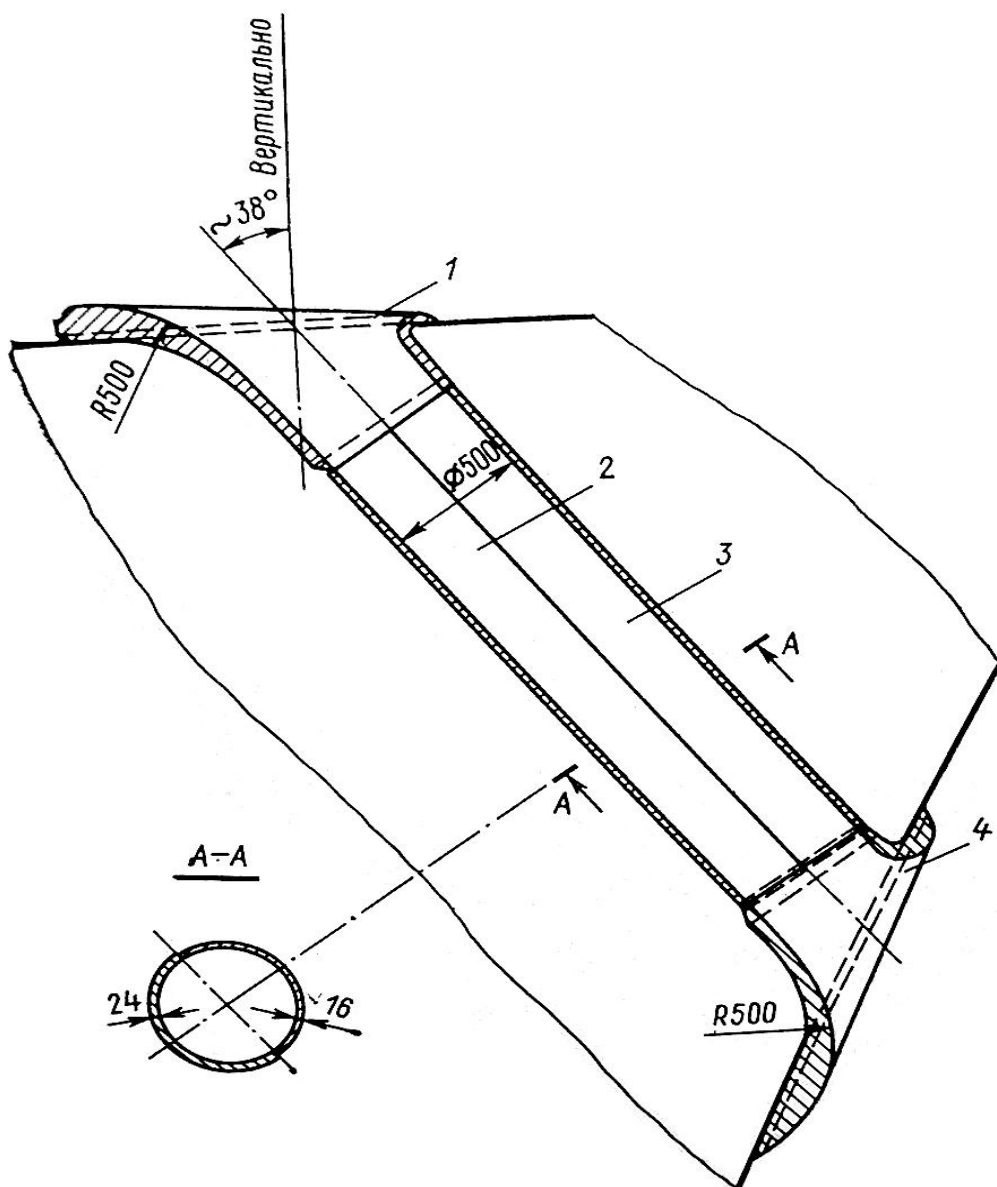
Наклонный якорный клюз для цепи калибром 49 мм:
